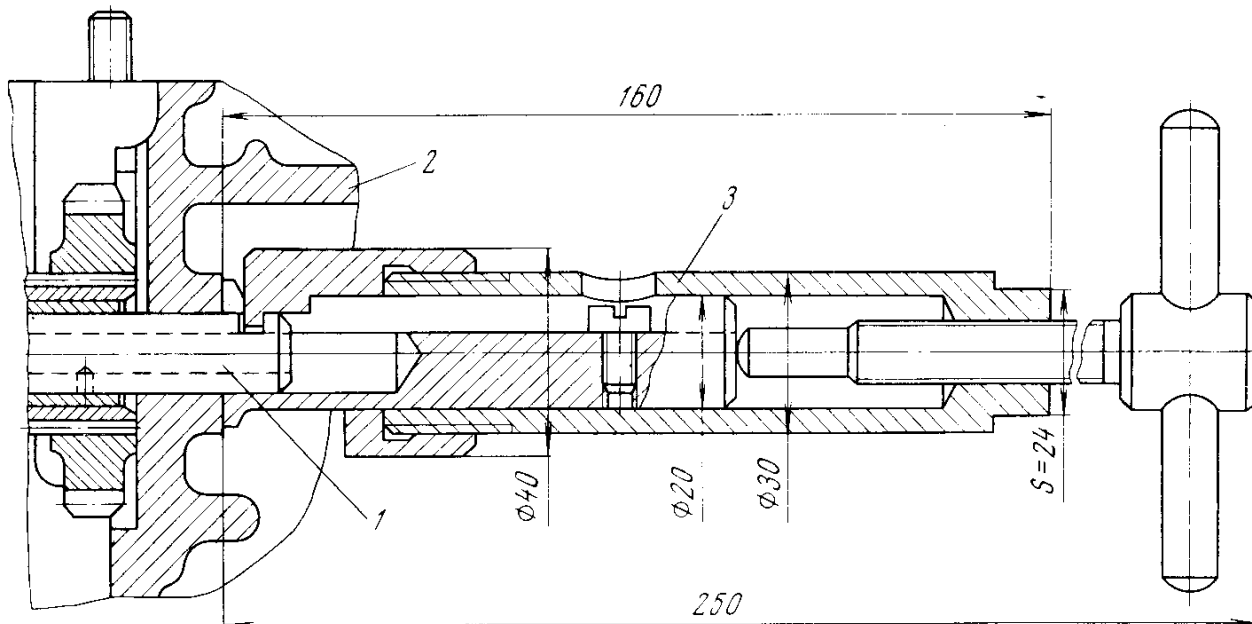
Съёмник оси шлицевого вала: 1 — ось шлицевого вала (вал условно повернут на 90°); 2 — картер коробки передач; 3 — съёмник.
